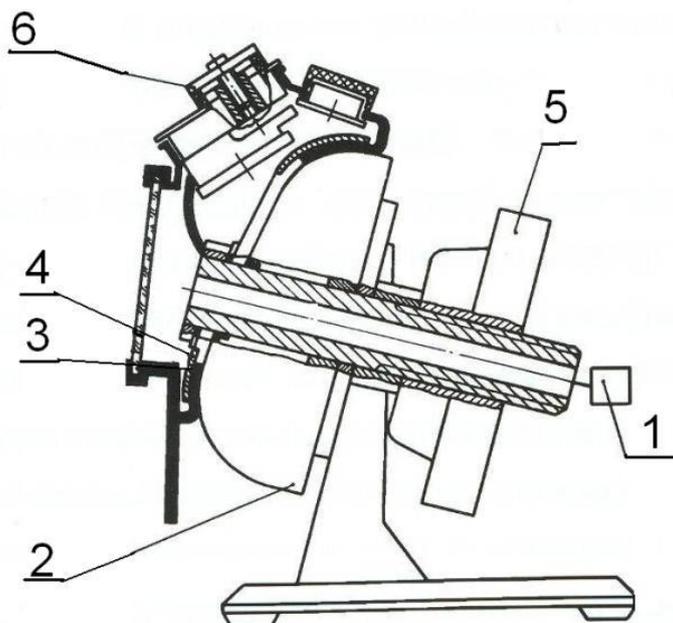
Схема с приспособлением ПМ-3 для проверки маски на герметичность
